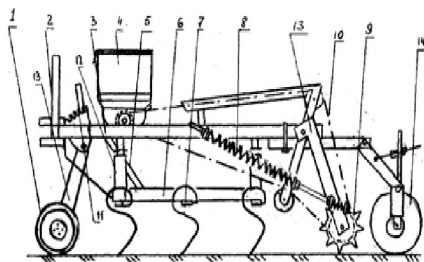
Схема комбинированного почвообрабатывающего агрегата: 1 – опорно-регулируемый каток; 2 – навесное устройство; 3 – рама; 4 – туковысевающий аппарат; 5 – тукораспределитель; 6 – рыхлительная секция; 7 - S-образный зуб; 8 – пружинный механизм; 9 – универсальный каток; 10 – цепная передача; 11 – сектор; 12 – подвеска рыхлительной секции; 13 – стойка; 14 – опорный каток.
